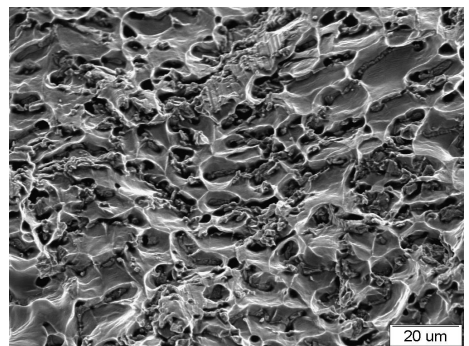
是2219T62铝合金VPTIG焊接接头的拉伸试样和断口形貌。
